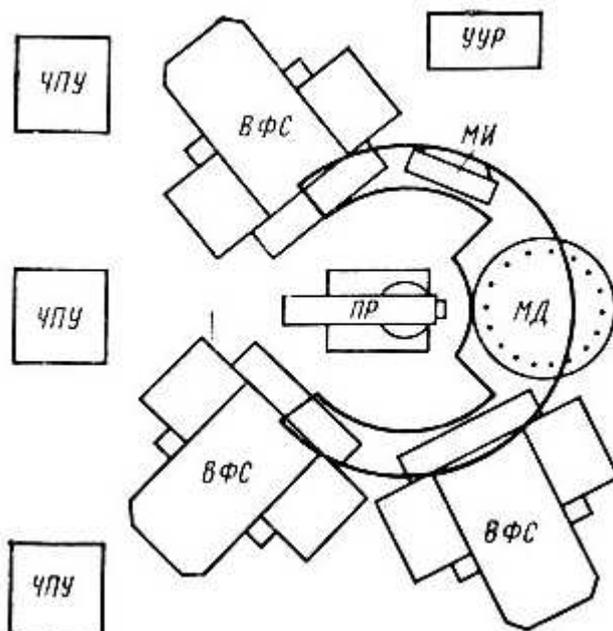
Компоновочная схема РТЯ: ПР - промышленный робот МП-8; ВФС - вертикально-фрезерный станок модели 6520Ф3; ЧПУ - устройство числового программного управления станком; УУР - устройство управления роботом; МИ - магазин инструмента; МД - магазин деталей, занимаемая площадь  $S = 29 \text{ м}^2$
